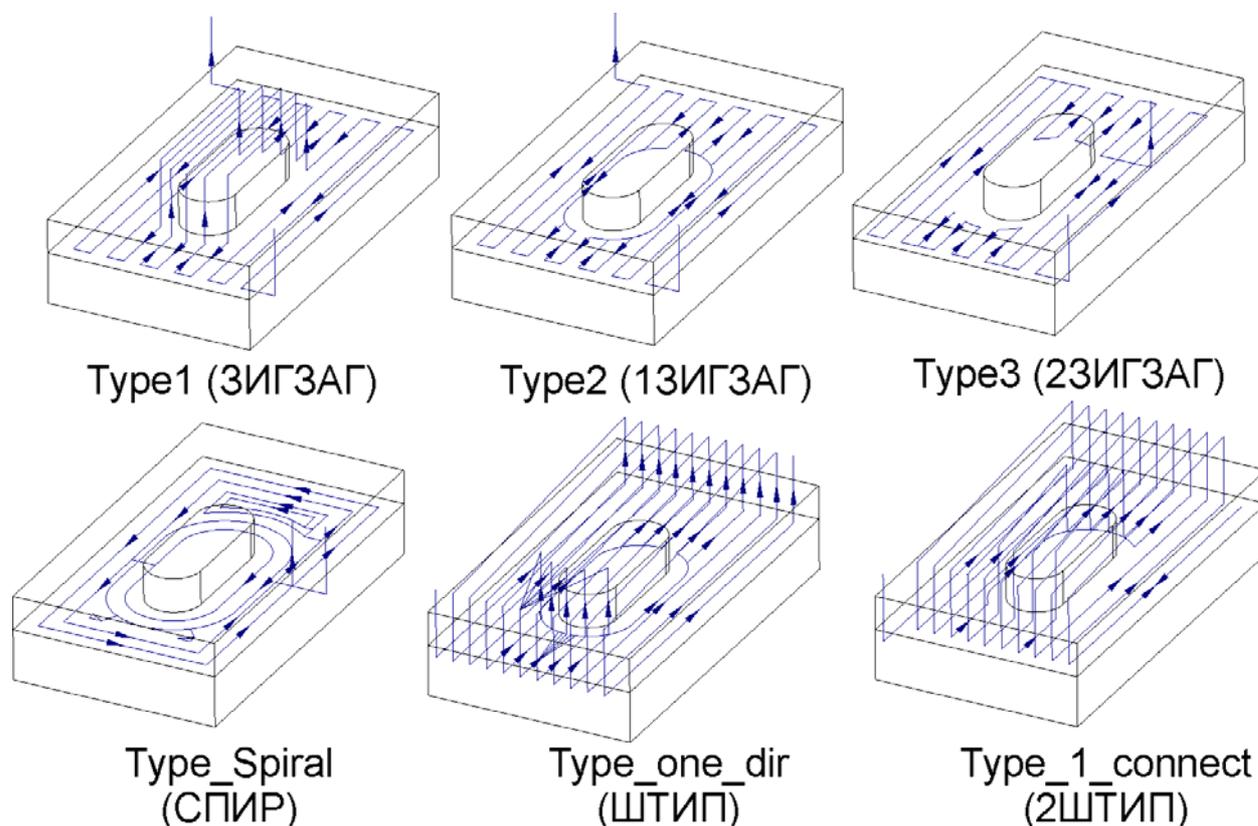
Основные стратегии черновой фрезерной обработки
